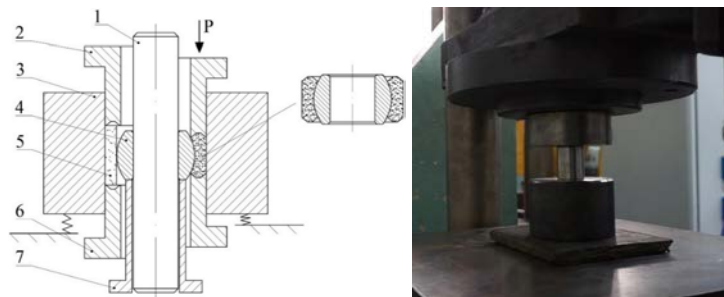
Схема пресс – формы и пресс для холодной штамповки:
